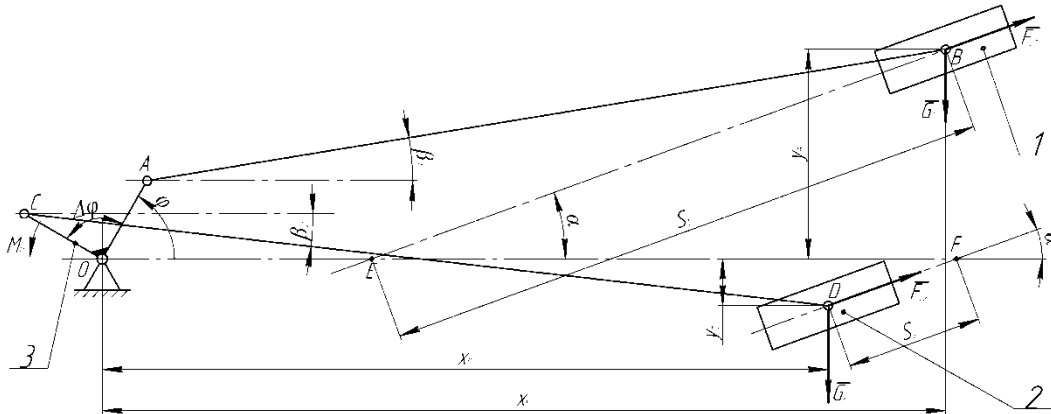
Кінематична схема приводного механізму решітних станів зерноочисних машин: 1 – верхній решітний стан; 2 – нижній решітний стан; 3 – ексцентрик
